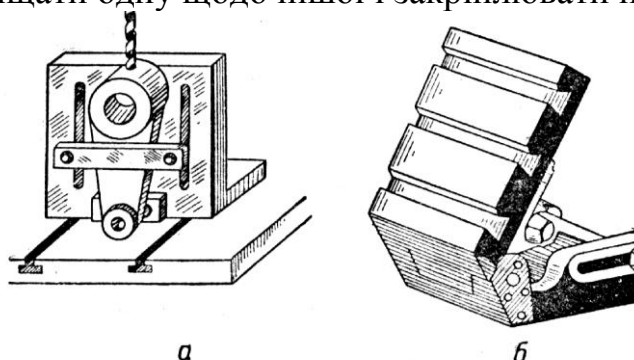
Косинці для закріплення деталей складної форми: а — звичайний; б — універсальний
